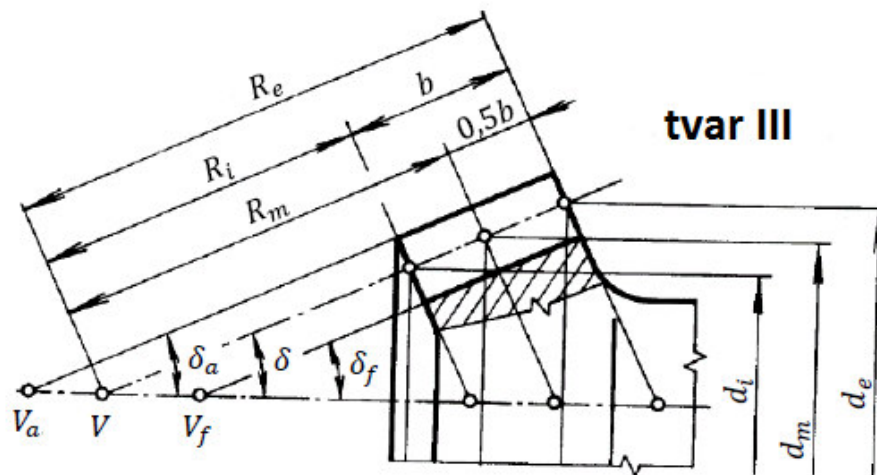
Kuželové soukolí se zakřivenými zuby. [12]
